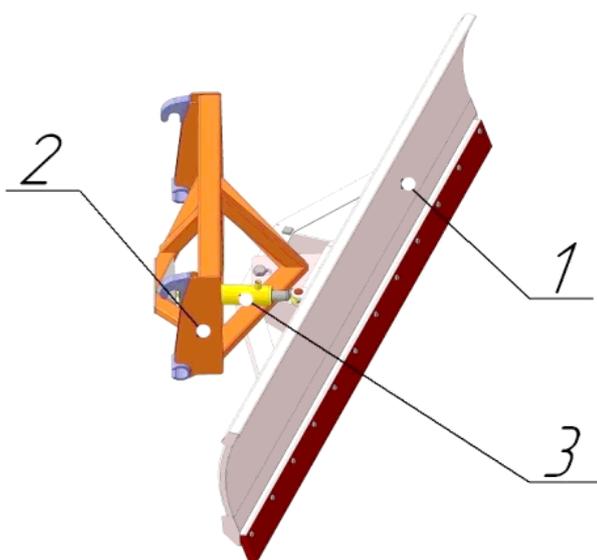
Общий вид и основные узлы Отвала снежного гидроповоротного 2,4м ПФН-150-03
